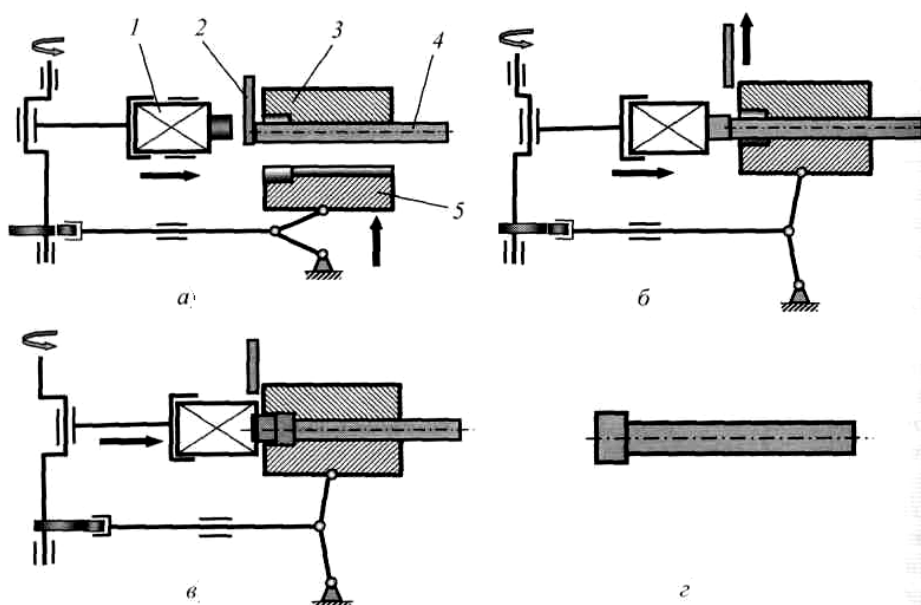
Етапи штампування на ГKM: *а* – встановлення заготовки, *б* – затискування заготовки в матриці, *в* – висаджування головки, *г* – готова заготовка;
